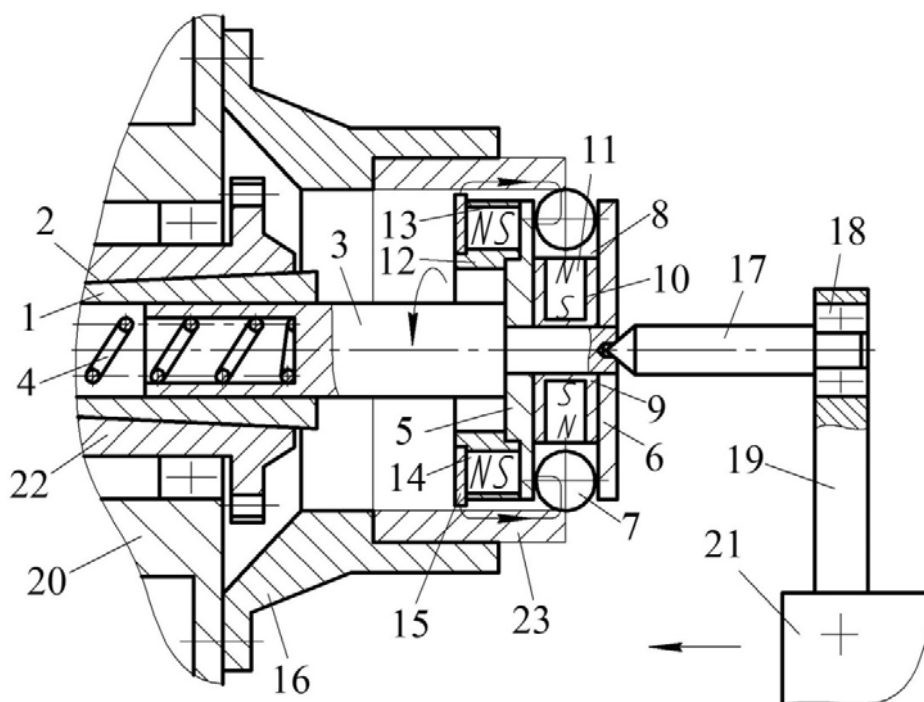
Инструмент для СМДН внутренней поверхности ферромагнитной втулки
